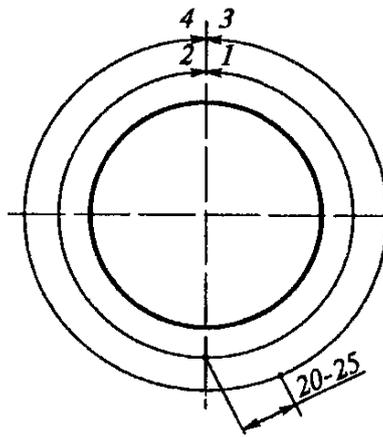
Порядок сварки неповоротного стыка труб
